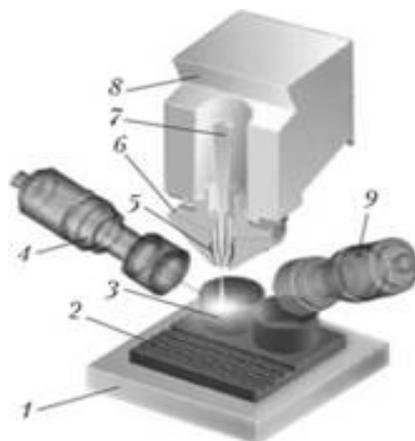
Схема процесса DMD: 1 – платформа; 2 – подложка; 3 – формирующаяся деталь; 4, 9 – оптическая система (видеокамеры); 5 – сопло вдува инертного газа; 6 – канал подачи порошка; 7 – луч лазера; 8 – фокусирующая оптическая система
